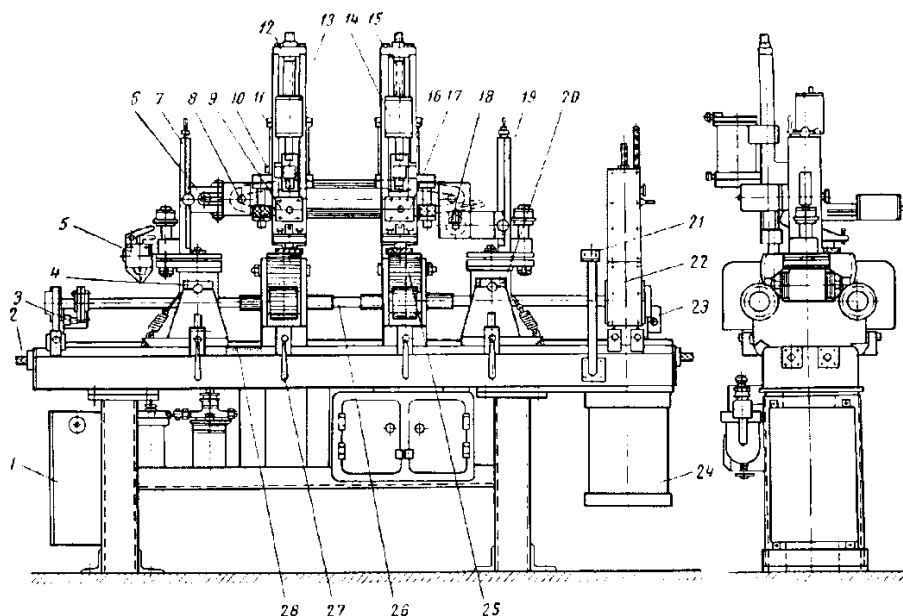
Полуавтомат для растяжки и формовки катушек статора.
